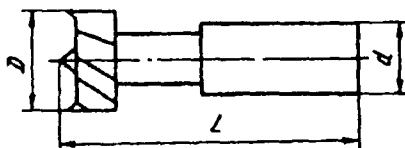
Сверло чашечное к станкам СВСА-2 и СВСА-3
